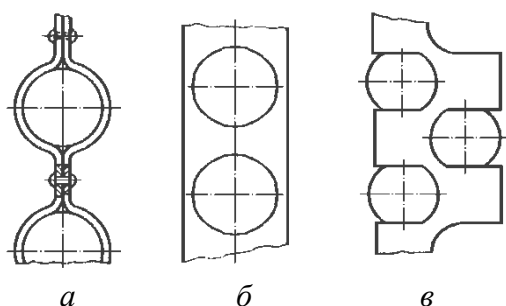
Конструкции сепараторов шариковых радиальных подшипников: а – штампованный (змейковый); б – массивный; в – лепестковый
